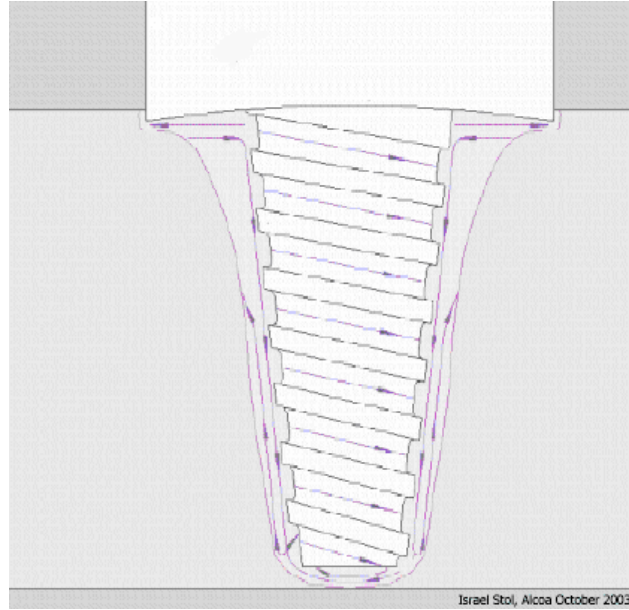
SKK Süresince Kaynak Dikişi Boyunca, Gelişme Bölgeleri [3].
